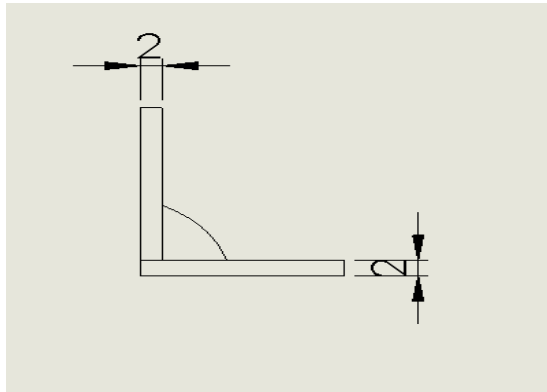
Diseño de junta soldada para placas de 2 mm. Fuente:
